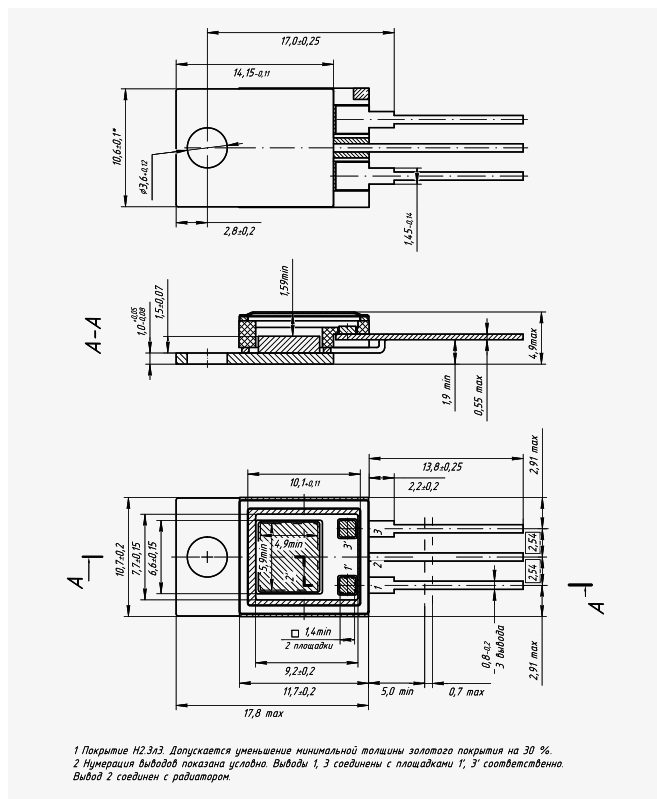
Габаритный чертеж металлокерамического корпуса KT-28A-4 K
